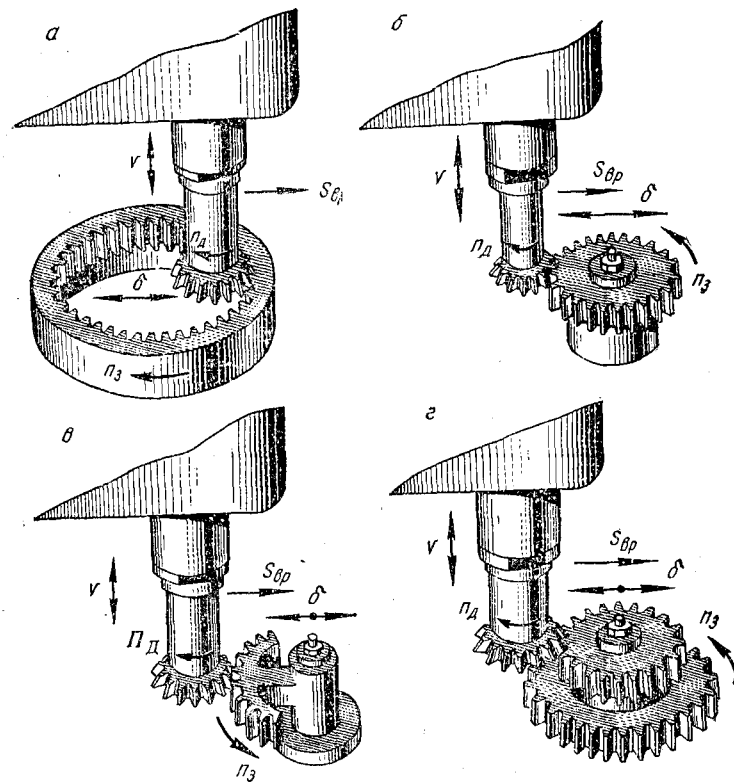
Схемы нарезания зубчатых колес зуборезным долбяком
